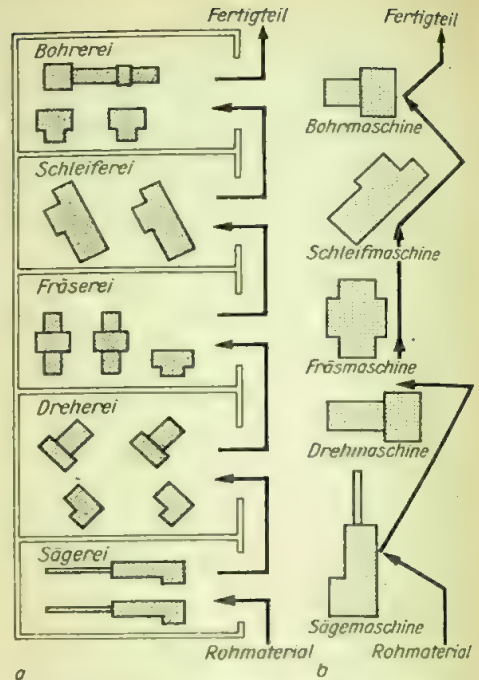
Anordnung von Bearbeitungsmaschinen: a Werkstätten-, b Gegenstandsprinzip
